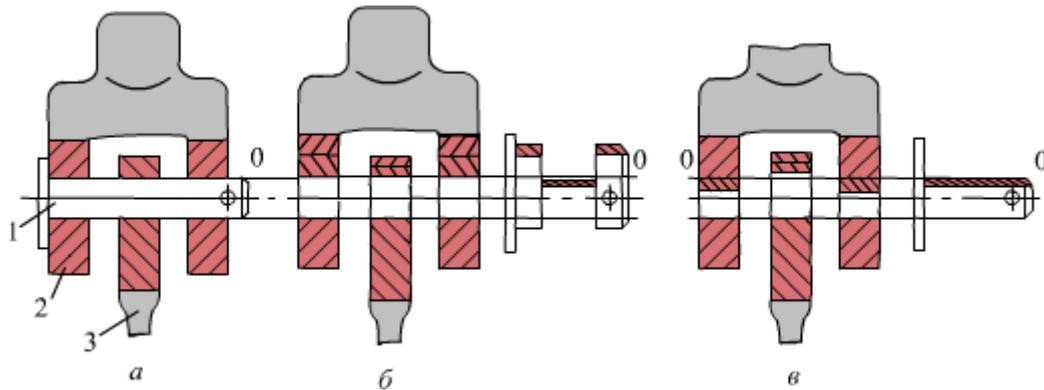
Шарнірне з'єднання вилки з тягою (форма валика і розташування полів допусків для наочності показані схематично):
